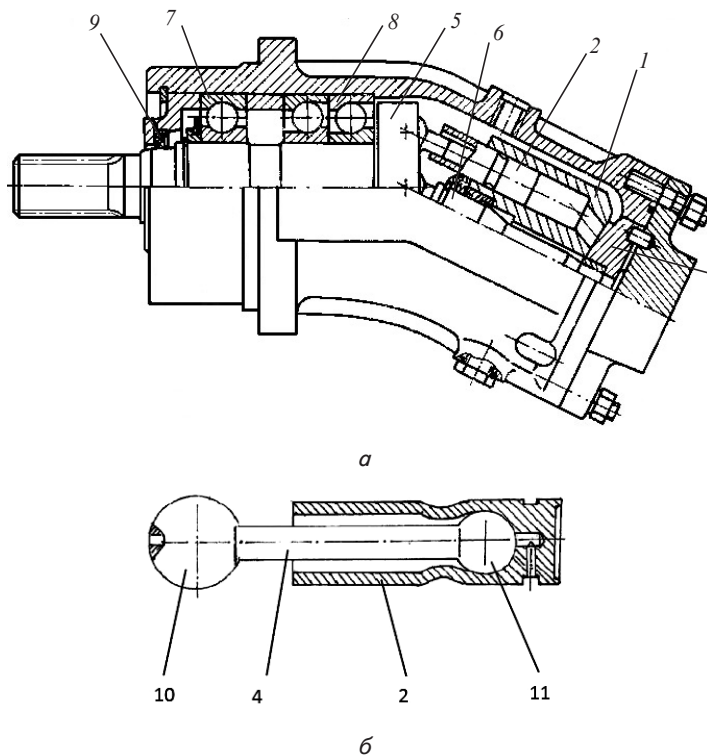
Аксиально-поршневая гидромашинка и ее основные пары трения: а – гидромашинка; б – поршень; 1 – блок цилиндров; 2 – поршень; 3 – распределитель; 4 – шток; 5 – опорный диск; 6 – шип; 7, 8 – подшипники; 9 – уплотнение; 10, 11 – сферическая поверхность
